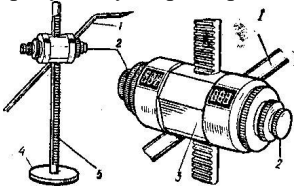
Мікрорейсмус з вимірювальними барабанами
